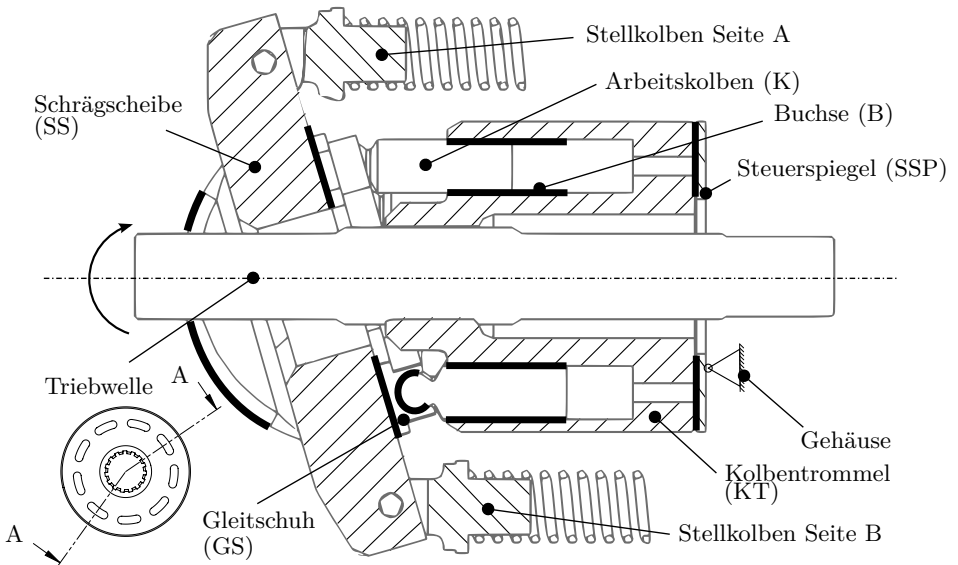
Schnittdarstellung einer Axialkolbenmaschine in Schrägscheibenbauweise mit den Haupttribokontakten
